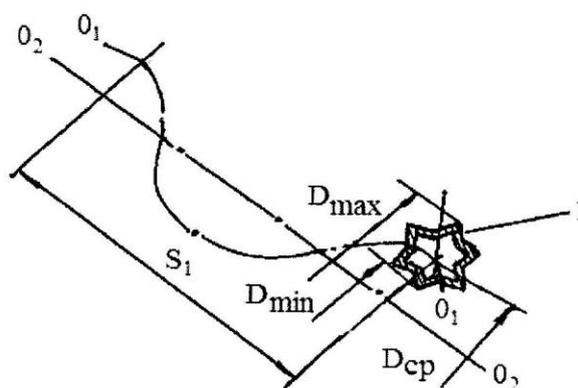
Схема изготовления рабочего органа станка для отделочно-зачистной и упрочняющей обработки деталей машин (1-поперечное сечение рабочего органа станка; D_{max} и D_{min} наружный и внутренний диаметры рабочего органа станка; D_{min} –внутренний диаметр рабочего органа станка; O_1-O_1 - ось симметрии спирального рабочего органа станка; O_2-O_2 – центральная прямолинейная ось рабочего органа станка; S_1 - шаг спирального рабочего органа станка)
